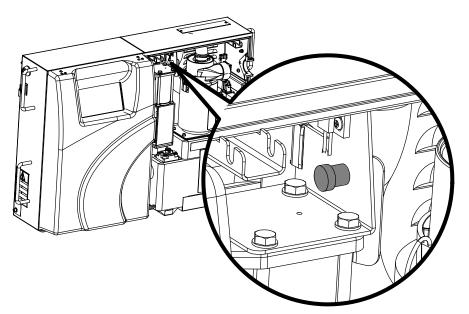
Position des federbelasteten Stifts zum Aufklappen der Hydraulikbaugruppe
